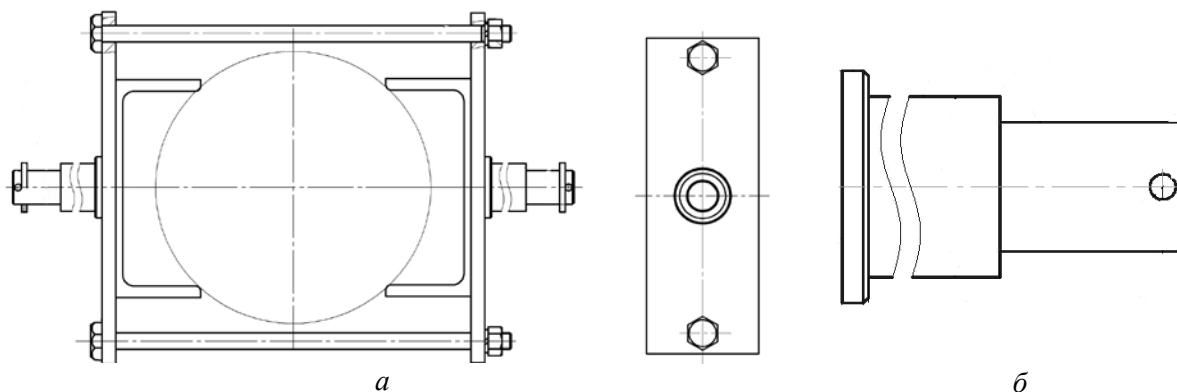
Фронтальный вид захвата гидроцилиндра ковша (а) и цапфы (б)
